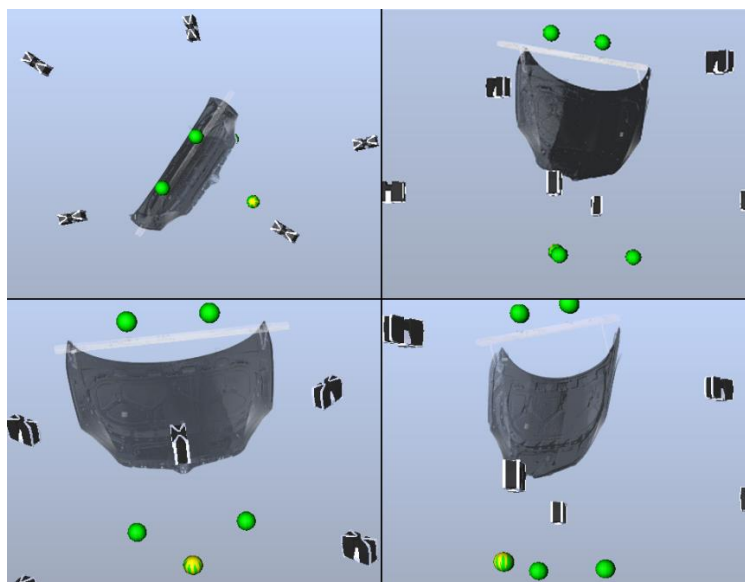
Prostorové uspořádání dílčích skenů kapoty
